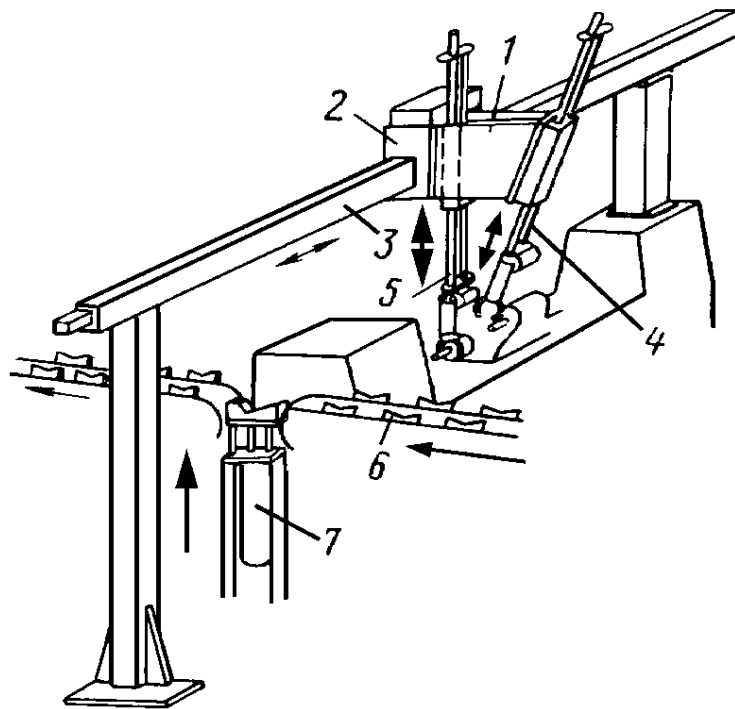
Установлення деталі на токарний верстат за допомогою механічної руки фірми Toshiba: 1 – кронштейн зі здовоною механічною рукою; 2 – рухома каретка для кріплення рук; 3 – напрямна, по якій рухається каретка; 4 – захоплювач руки для заготовок; 5 – захоплювач руки для готових деталей; 6 – ланцюговий транспортер з електроприводом; 7 – механічна рука – підйомник заготовок з транспортера
